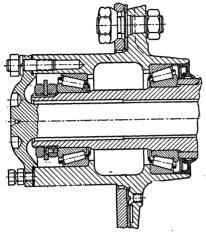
Опоры заднего колеса грузового автомобиля на конических подшипниках
